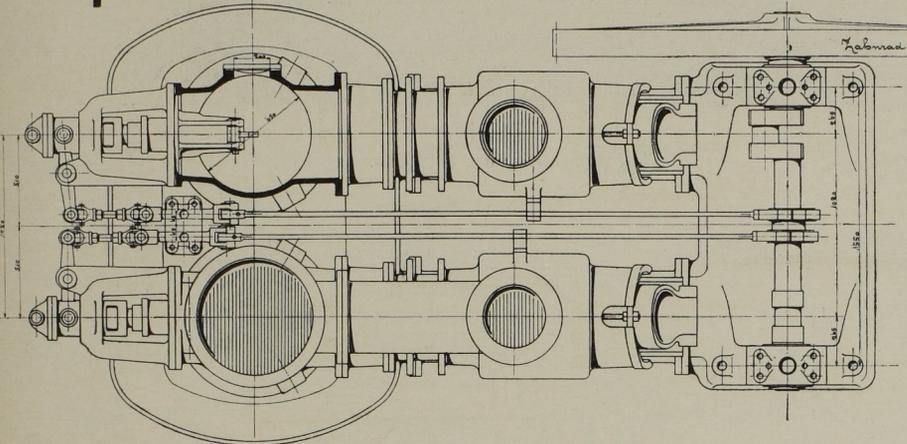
Grundriss der Pumpe. Massst. 1 : 40.
